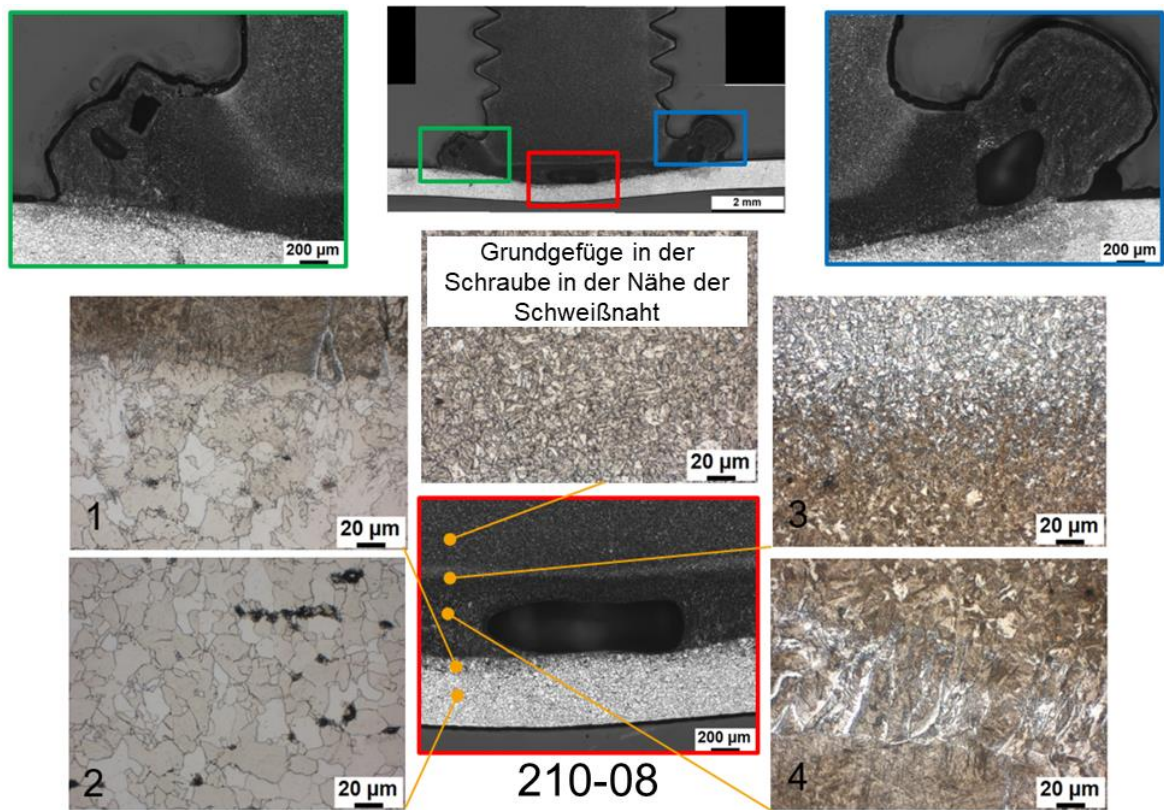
Mikrostruktur und lokale Geometrie der Schweißnaht der Bolzenprobe 210-08
